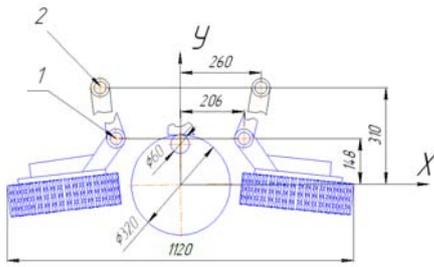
Схема компоновки захватных рычагов с вальцами: 1 – расположение шарниров «рычаг – корпус» в расчетном варианте; 2 – расположение шарниров головки Kesla Foresteri 18RH
